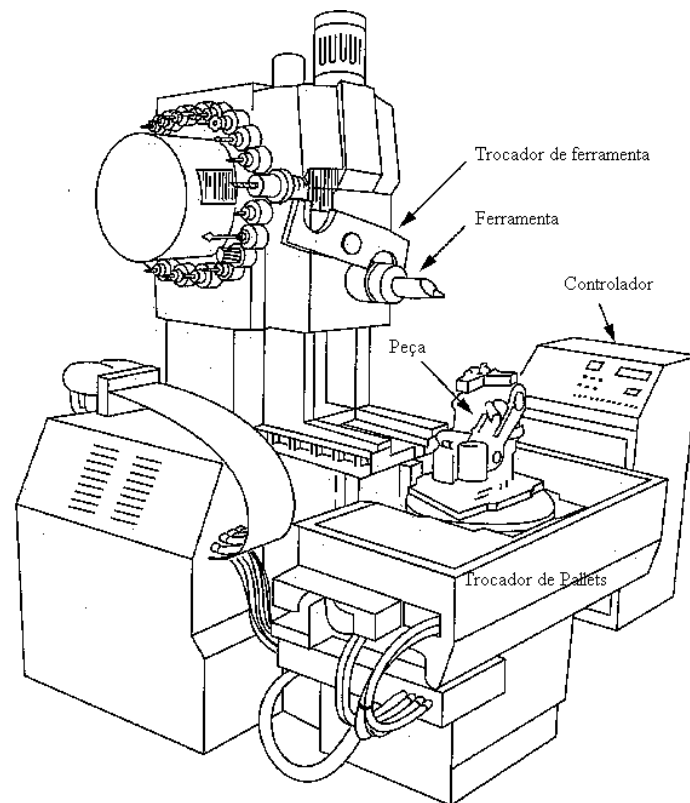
O centro de usinagem CNC permite operações de usinagem muito diferentes a serem executadas num único setup
